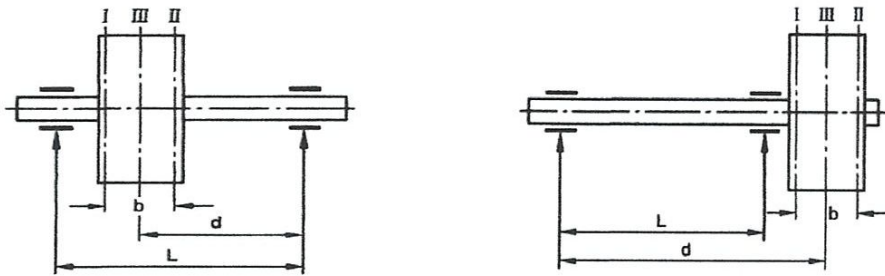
Faible écartement des plans de correction situés entre les paliers
